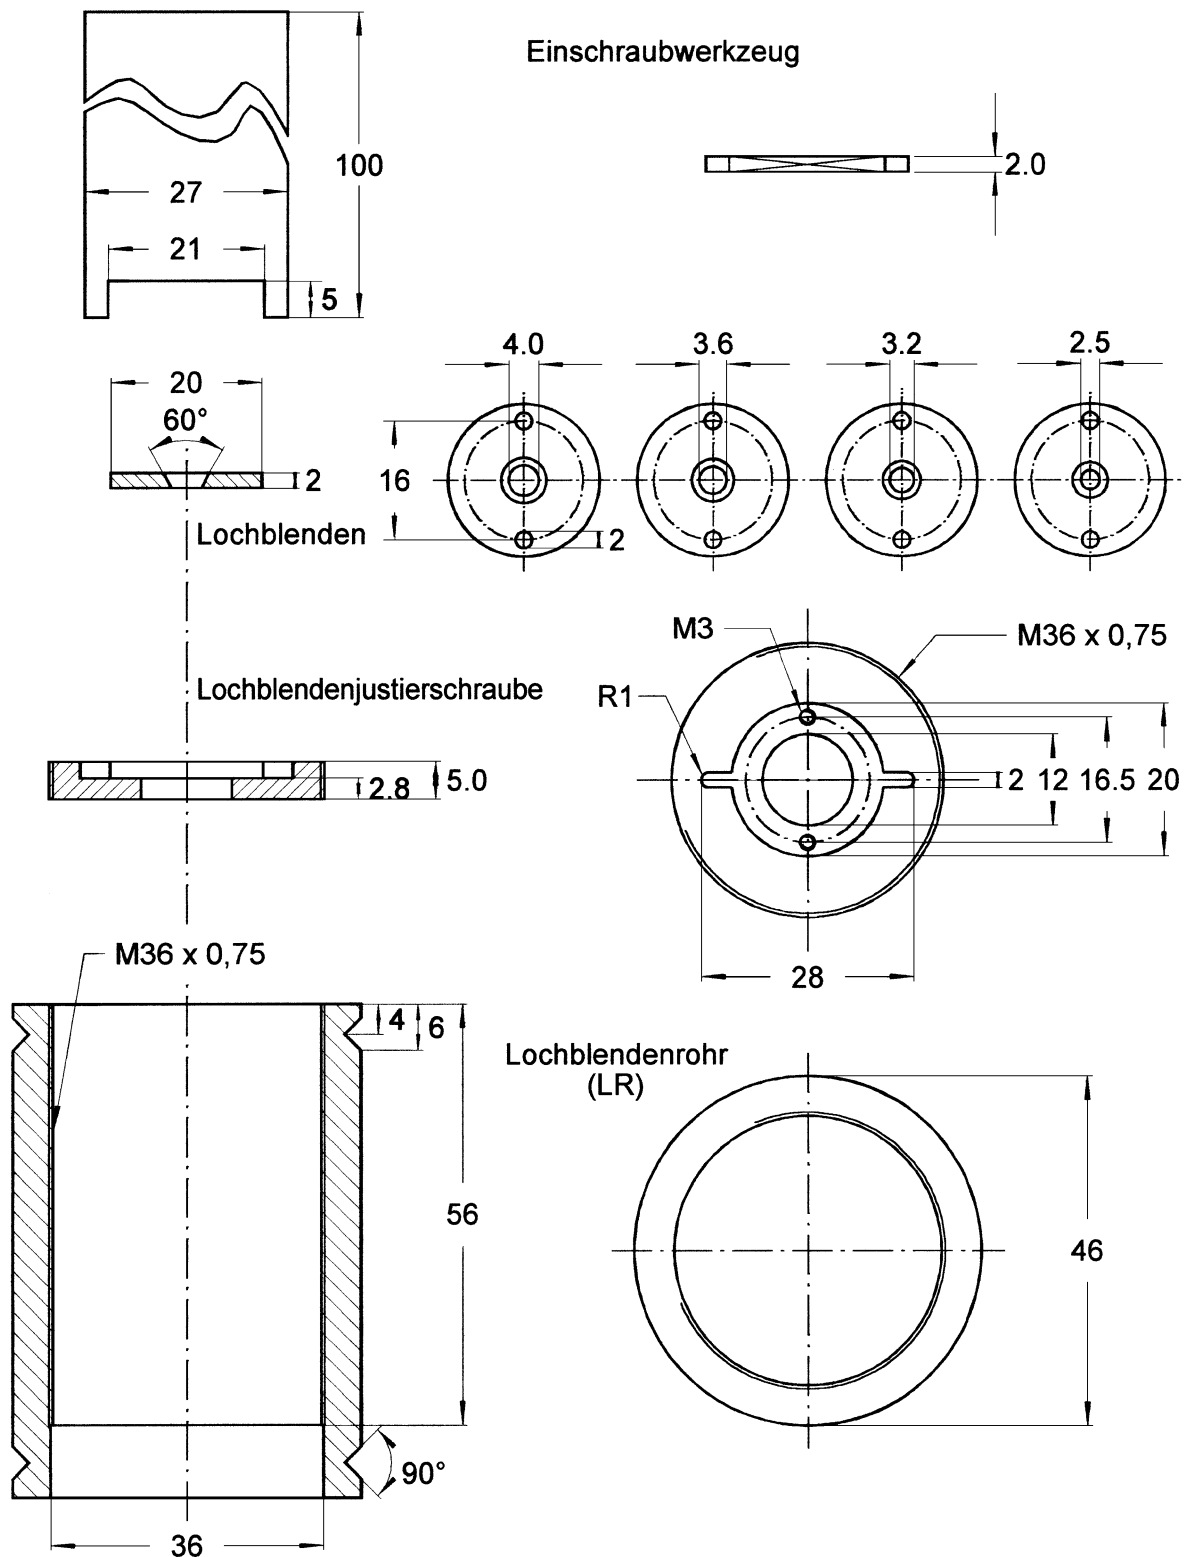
Lochblendenrohr mit Justierschraube für verschiedene Lochblenden und zugehörigem Einschraubwerkzeug (Bezeichnung: LR).
